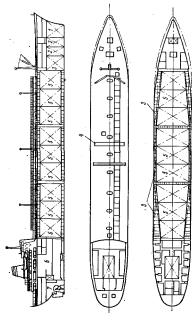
Схема общего расположения метановоза «Methane Princess».
